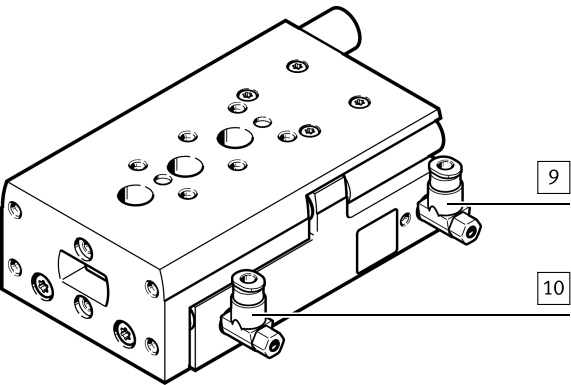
Druckluftanschlüsse mit Drossel-Rückschlagventilen
